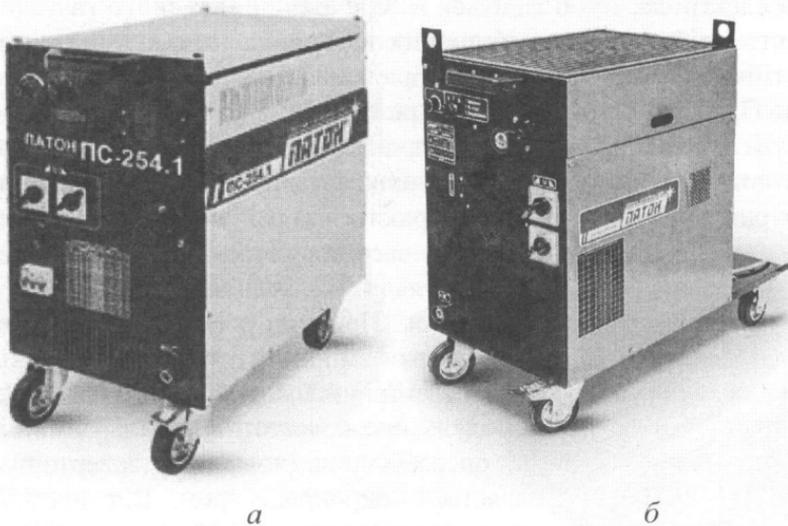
Зварні інвентарні напівавтомати однокорпусні (бренд Патон): а - 254.1 ; б - PC-350.1 DC
